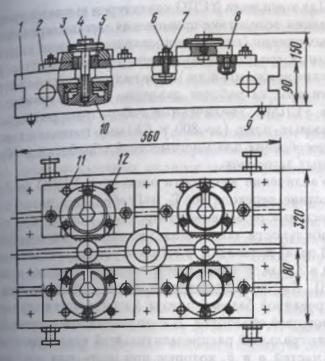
Пример приспособления системы СРП – ЧПУ
